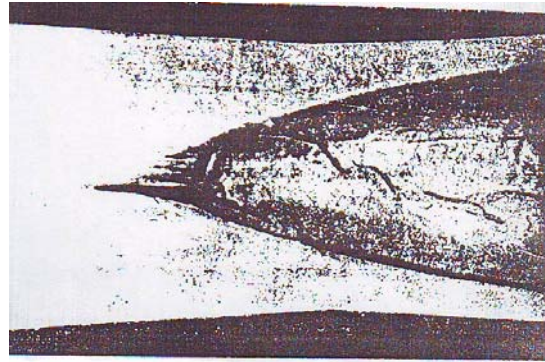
Мгновенный очаг деформации в процессе прошивки на прошивном стане трубопрокатного агрегата согласно[3]
